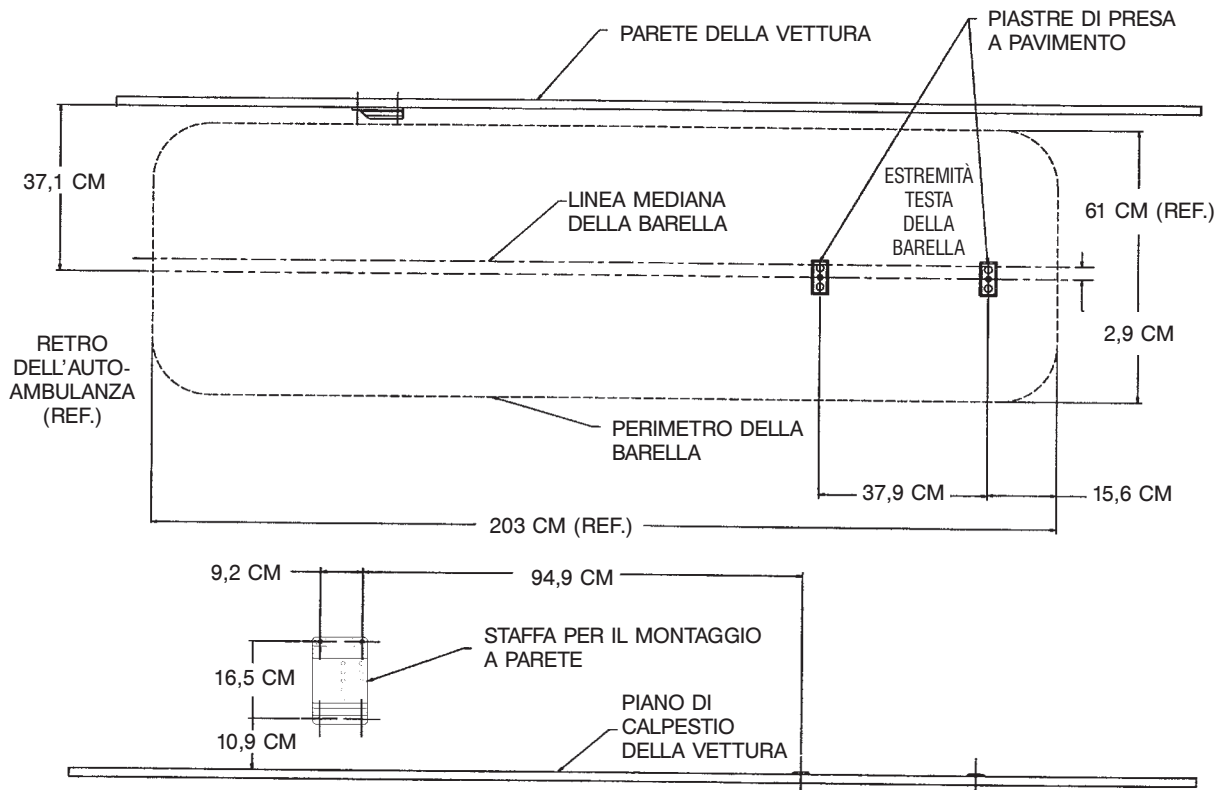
Dati tecnici di installazione - Sistema di ancoraggio a parete
